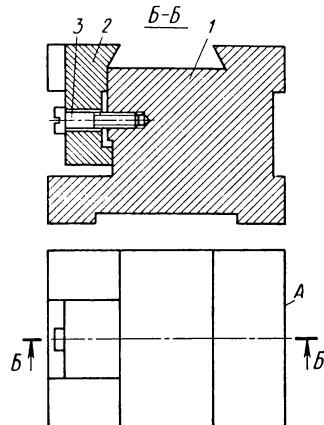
Приспособление для закрепления призматических резцов при шлифовании режущей части:
